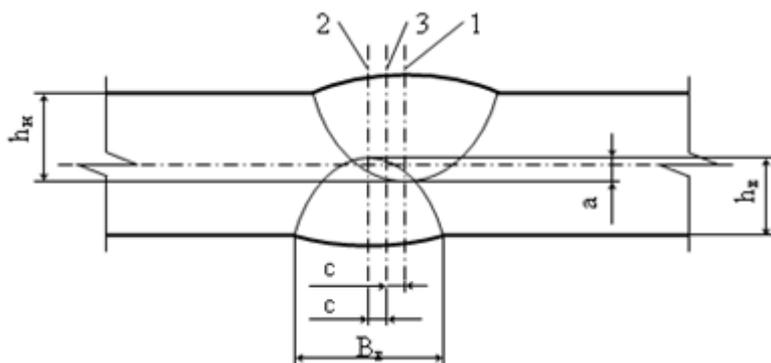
Макрошлиф для оценки геометрических параметров сварного шва: 1 – ось первого (наружного) слоя шва; 2 – ось внутреннего слоя шва; 3 – условная ось стыка; а – перекрытие наружного и внутреннего слоев шва ($a \geq 3$ мм при толщине стенки труб 12 мм и более; $a \geq 2$ мм при толщине стенки труб менее 12 мм; с – смещение осей первого наружного и внутреннего слоев шва от условной оси стыка ($c = \pm 1$ мм);
